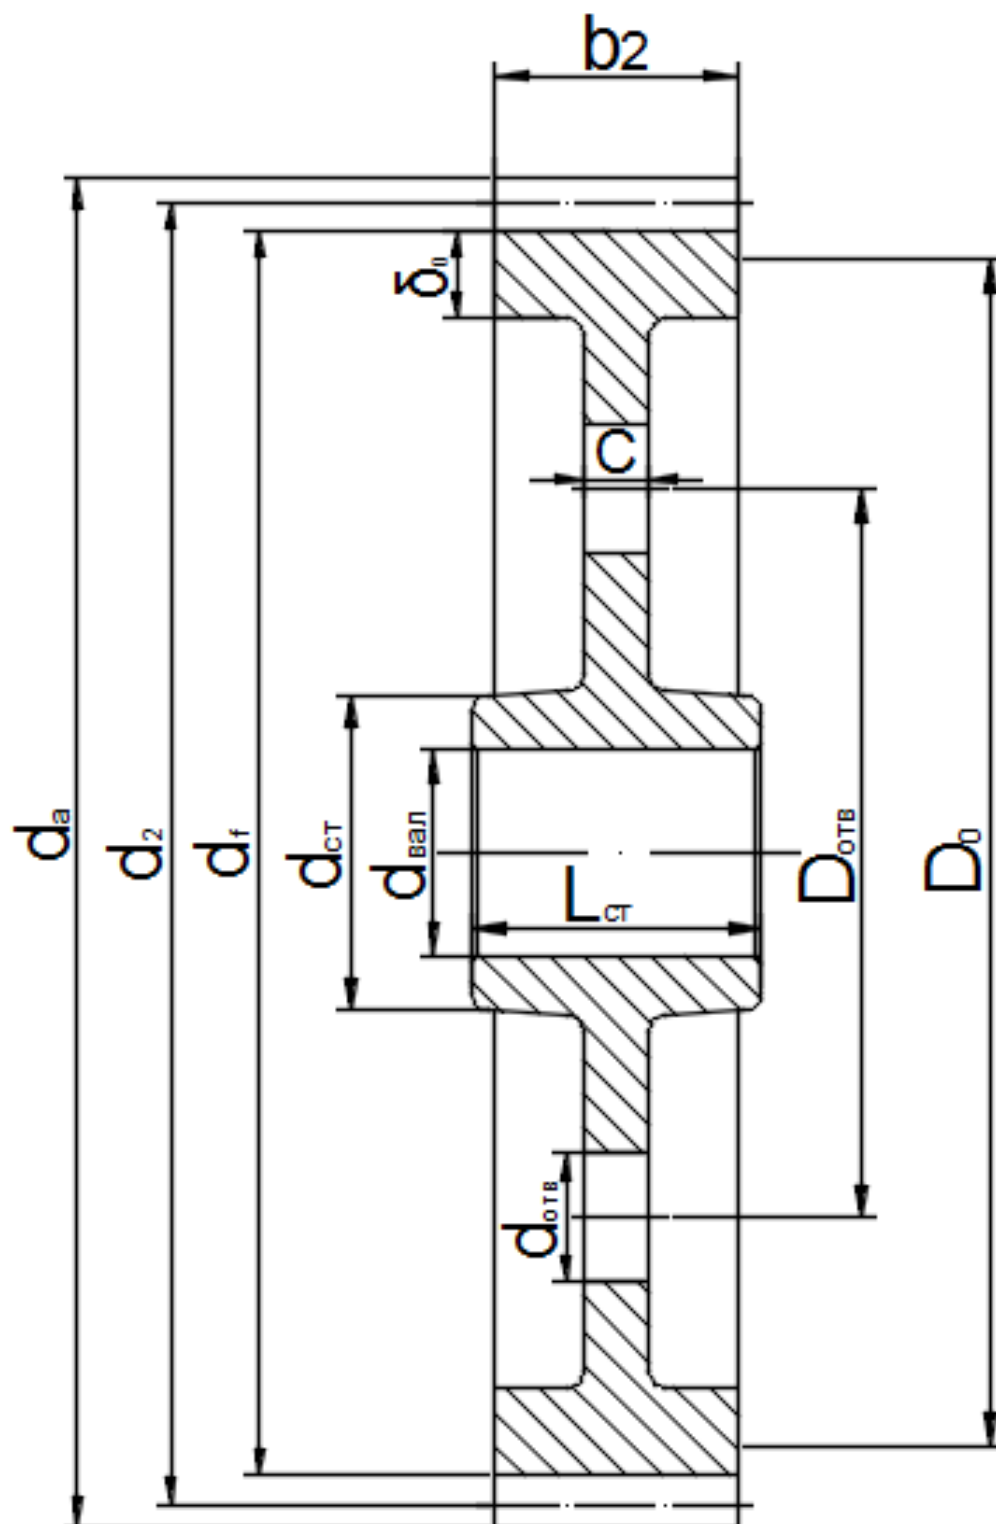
Конструктивные размеры цилиндрического зубчатого колеса
